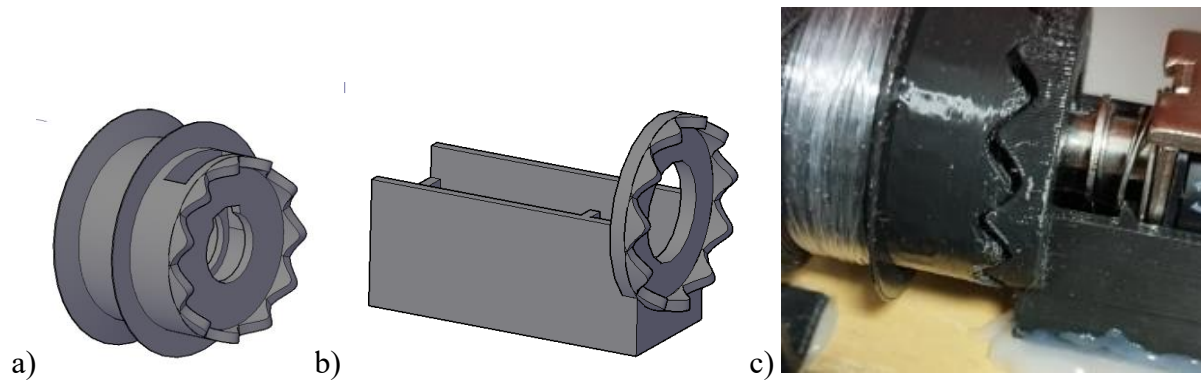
a) Engrane del tambor, b) Engrane del soporte del actuador, c) Acople entre ambos engranes.
